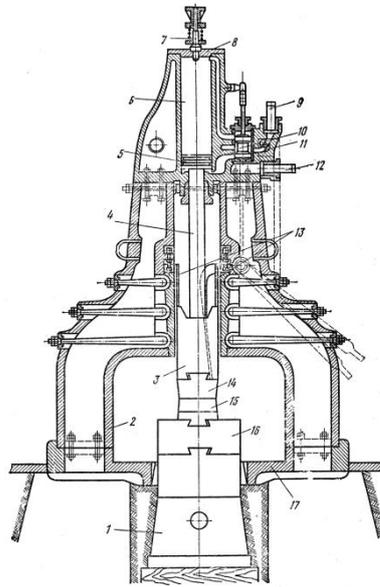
Паровоздушный двухстоечный ковочный молот двойного действия со станиной арочного типа:
